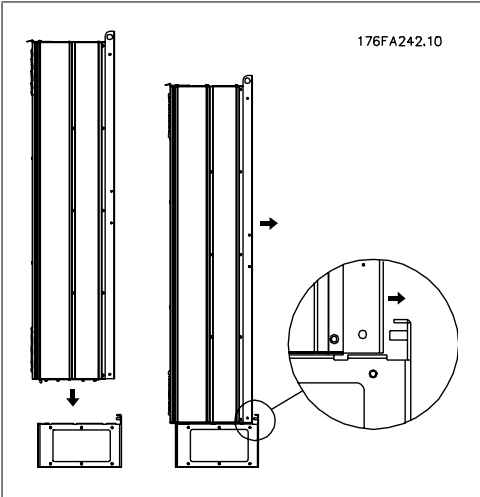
Montering af frekvensomformerer til sokkelen.
